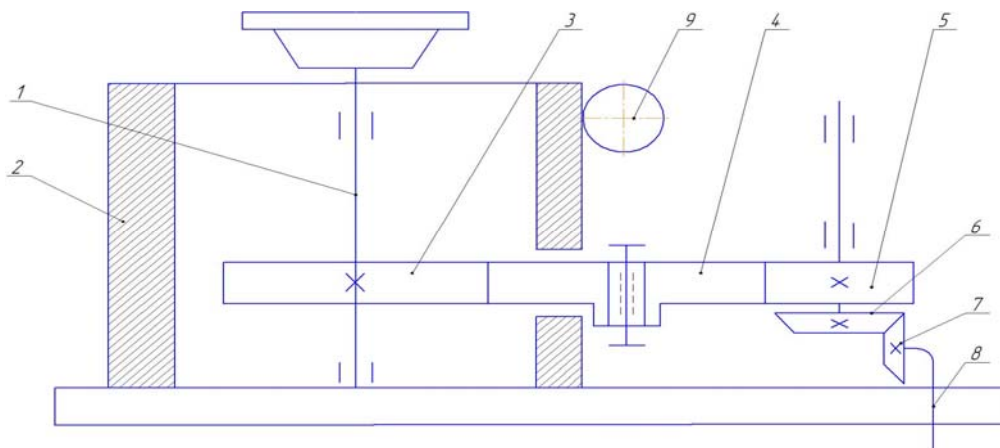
Кинематическая схема инструментальной головки и цилиндрической передач:
